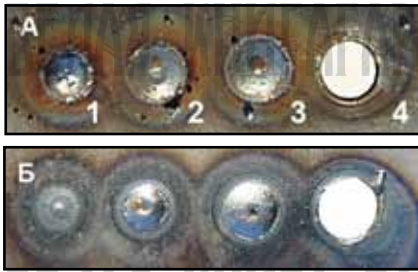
Подбор сварочного тока, А - вид со стороны сварки, Б - вид с обратной стороны металла.
